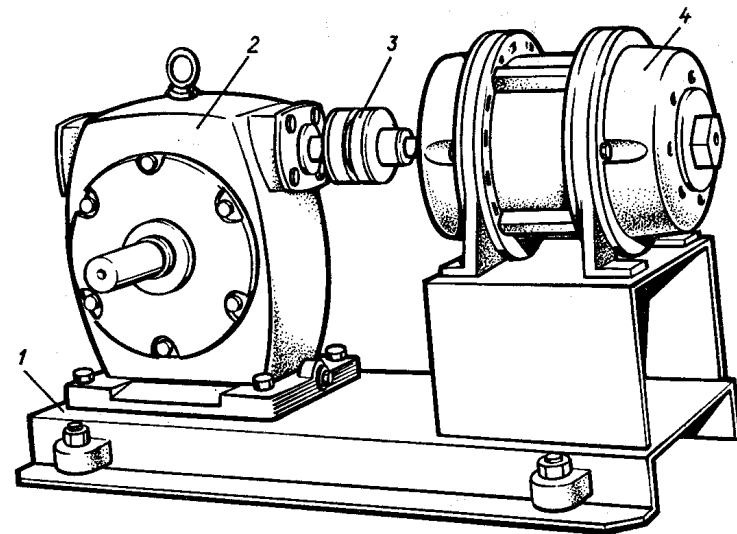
Установка привода на сварной раме из листовой стали:
